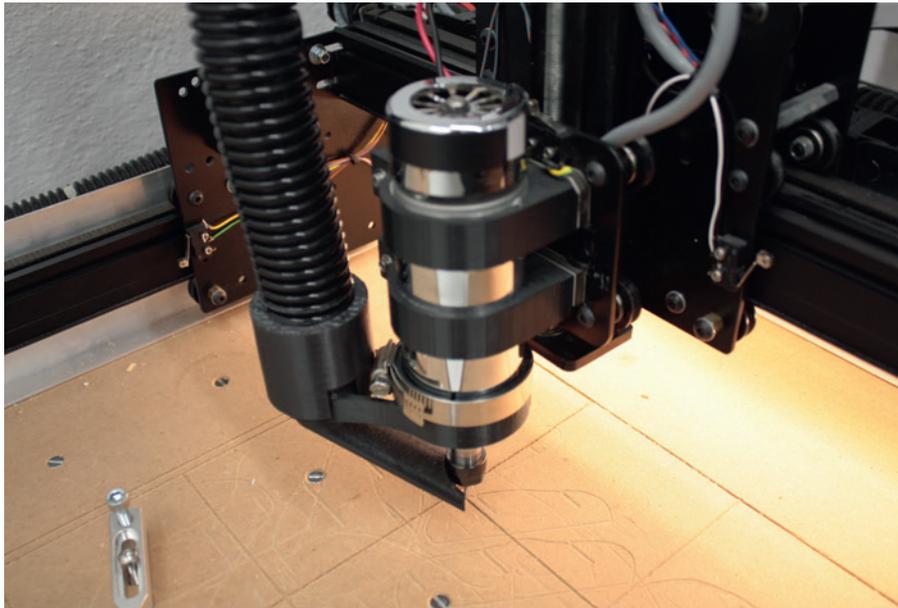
Ein 3D-Druckteil aus Thingiverse mit selbst modelliertem Adapter bietet Platz zum Schauen und zum Wechseln der Werkzeuge.
